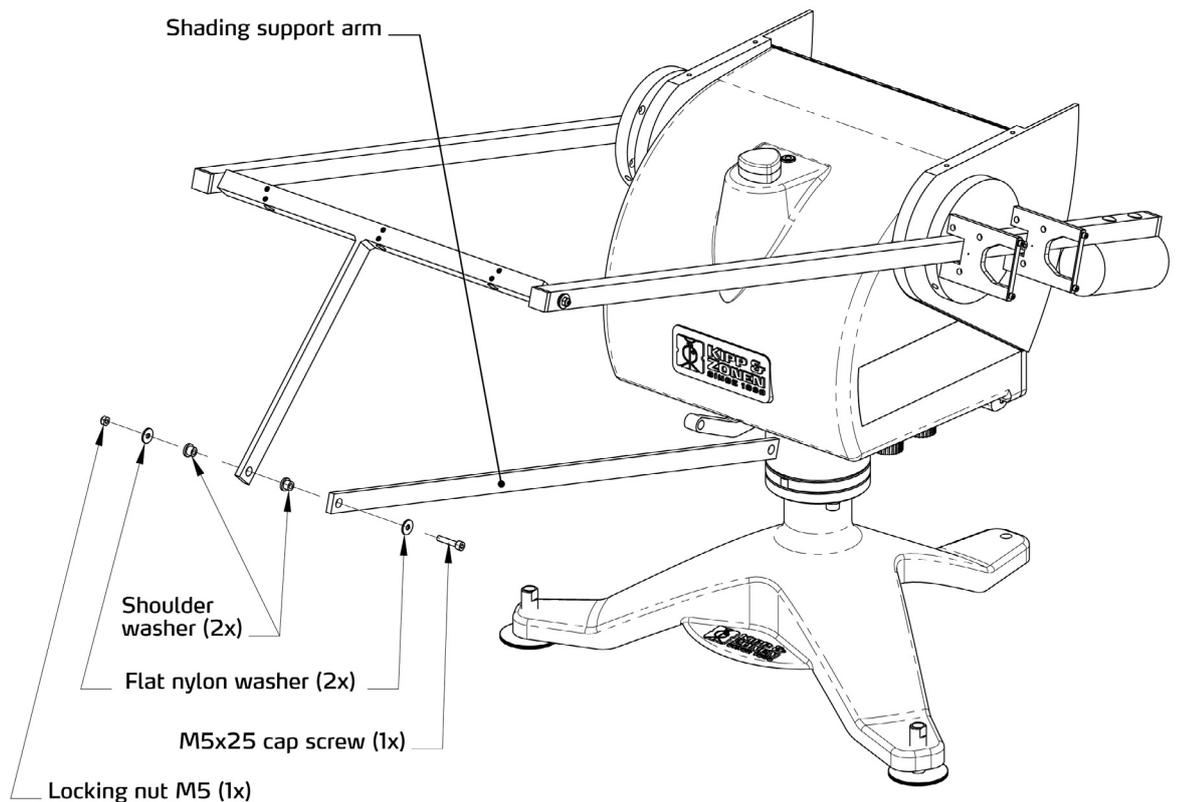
Montaje de la pieza superior del brazo de plato de sombra
